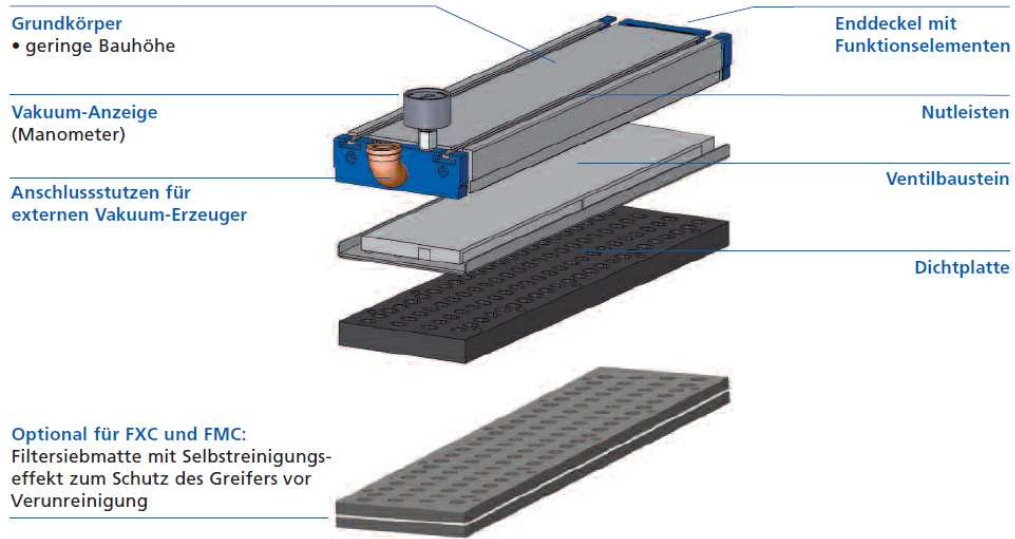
Flächengreifsystem mit externen Vakuum Erzeuger
